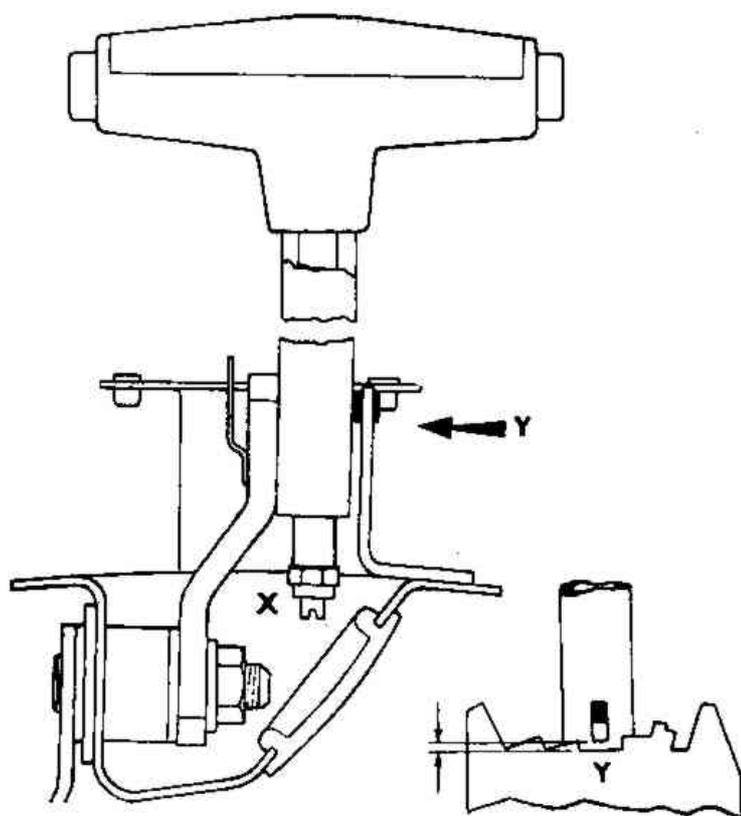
Регулировка контргайки (X) для получения точного зазора (Y) (Разд.12)
